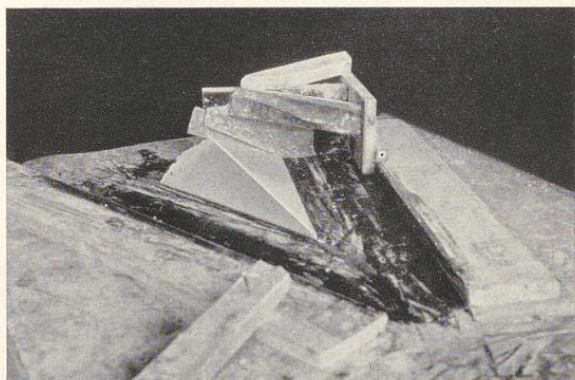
Verjüngter Zug einer Sternspitze mit halber Schablone
